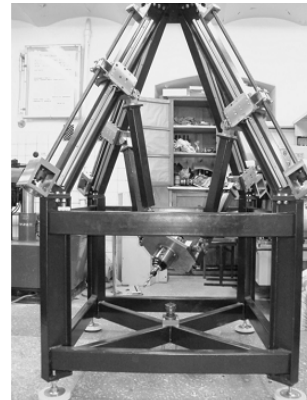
П'ятикоординатний свердлильно-фрезерний верстат каркасної компоновки з МПС (КПІ)
